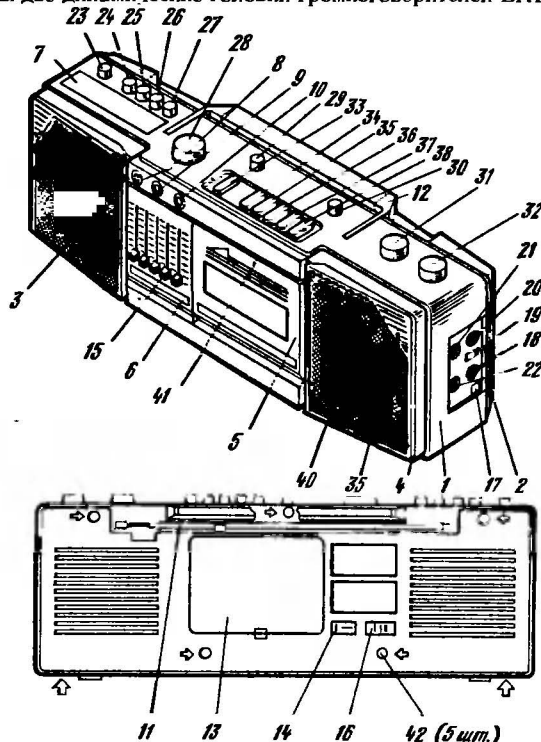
Внешний вид магнитолы «Соната РМ-323С»:
